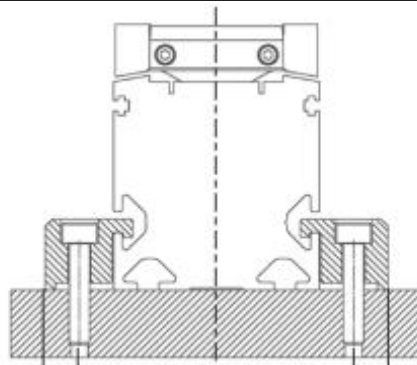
Disegno dimensionato di una staffa di fissaggio lunga
